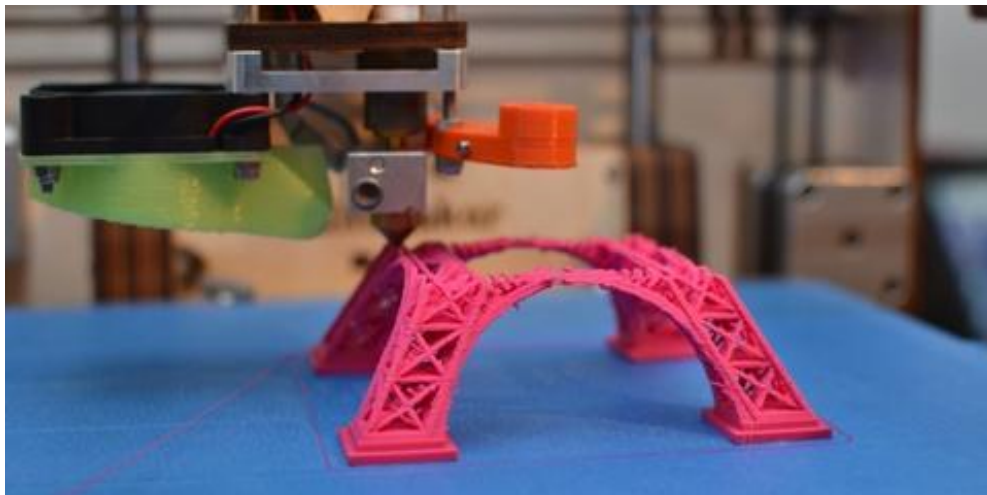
Impresión SLS. Adaptado de Impresoras3D.com
